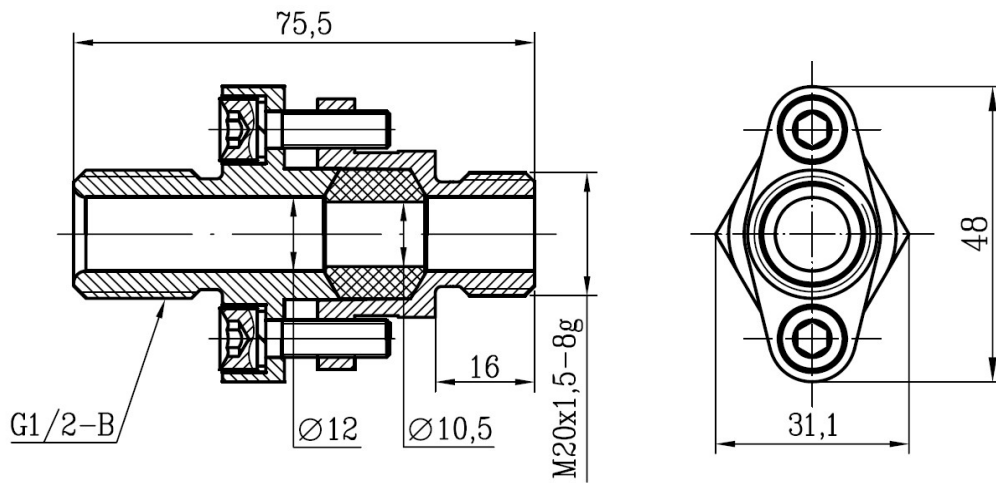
Ввод кабельный для трубного монтажа (ТБ 1/2")
